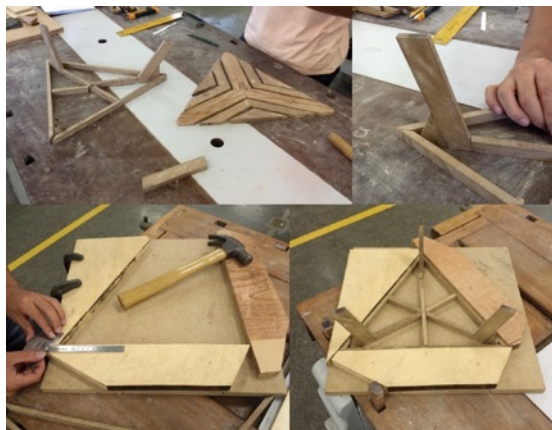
Pré-montagem do modelo; construção do gabarito de madeira para estabilizar as peças durante a colagem. Fonte: Autores.
